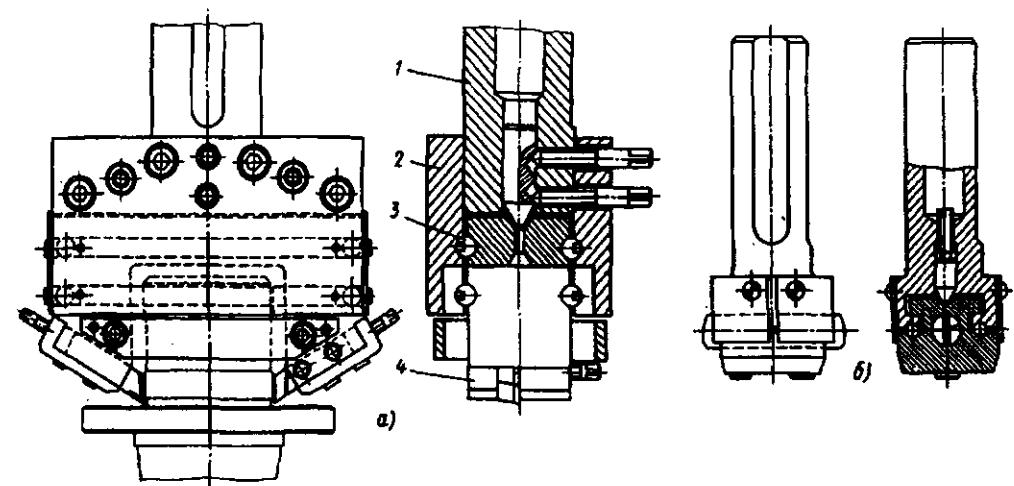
Плавающая головка конструкции ЗИЛ: а – для наружного обтачивания; б – для растачивания внутренних поверхностей (отверстий)
